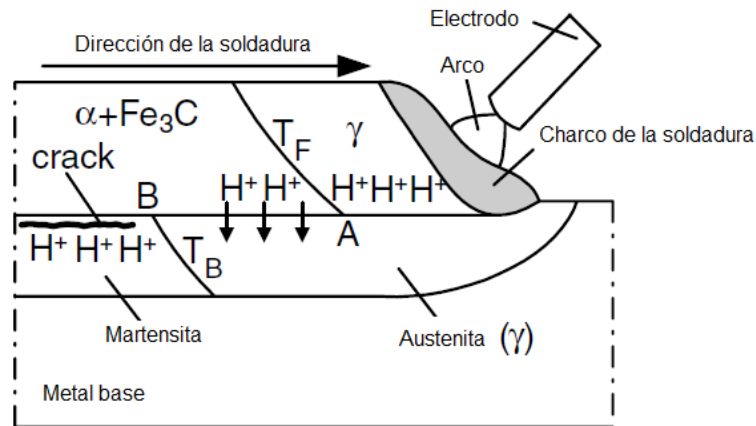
18 Difusión del hidrógeno desde el metal base a la ZAC durante la soldadura (27).
